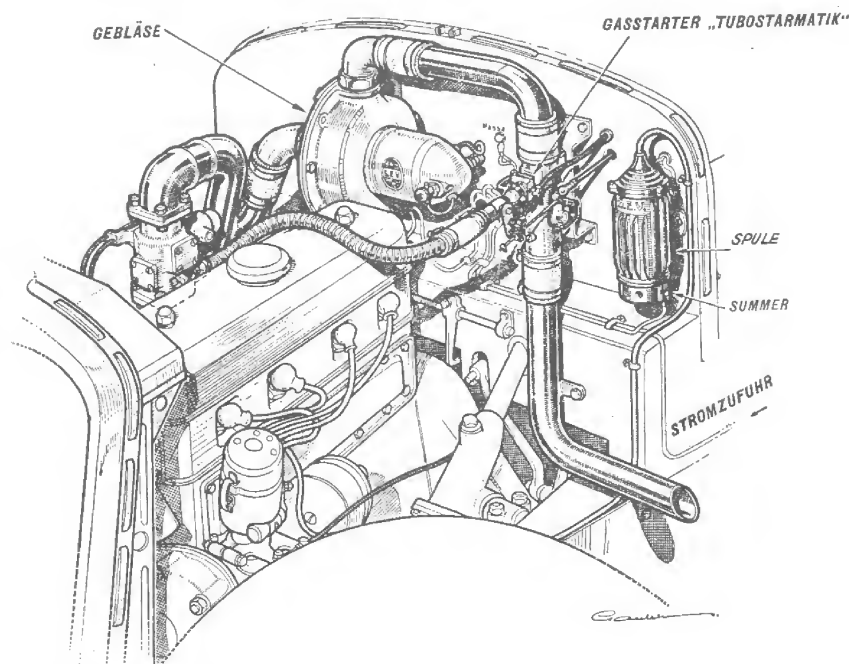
Blick unter die Motorhaube eines mit dem Gasstarter „Tubostarmatic“ ausgerüsteten Motors
